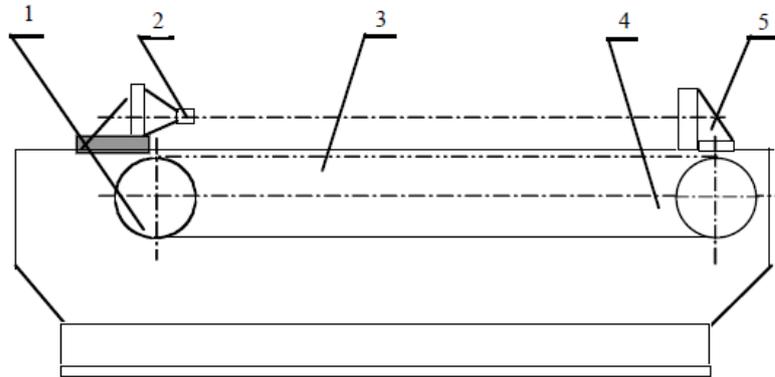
Máquina de corte longitudinal com jogo de facas tipo estrela.
